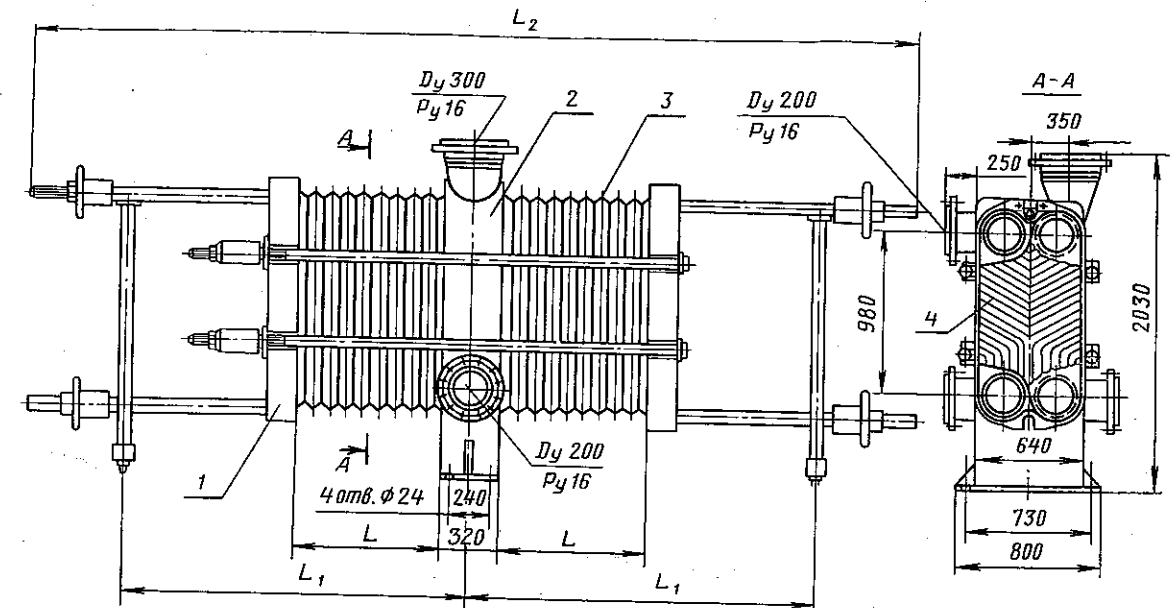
Общий вид теплообменника (конденсатора) с центральной неподвижной плитой (исполнение III); габаритные и присоединительные размеры:
